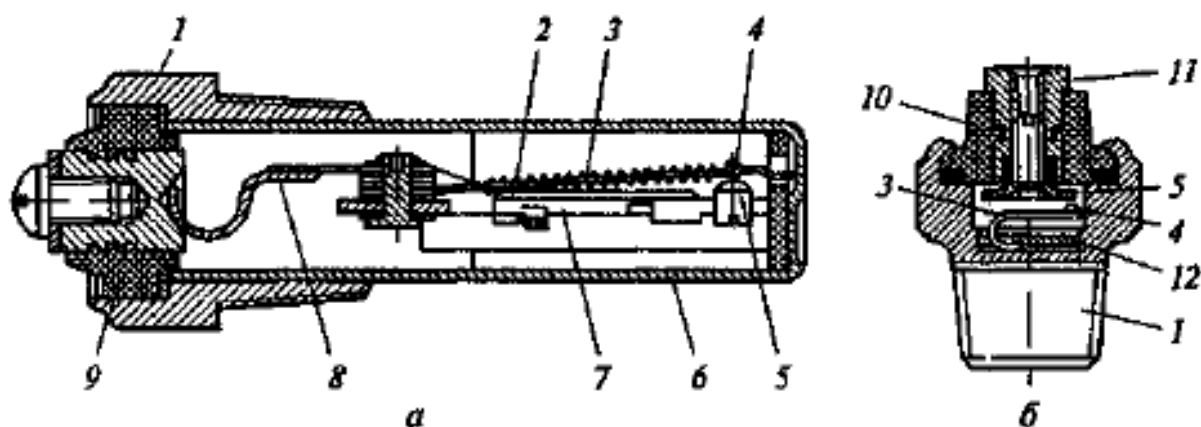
Датчики температуры: а – термобиметаллический импульсный; б – сигнализатор аварийной температуры; 1 – корпус; 2 – обмотка нагревателя, 3 – биметаллическая пластина; 4 и 5 — контакты (подвижный и неподвижный); 6 – баллон; 7 – кронштейн; 8 – токоподводящий контакт; 9 – основание; 10 – втулка; 11 – зажим; 12 – шайба
